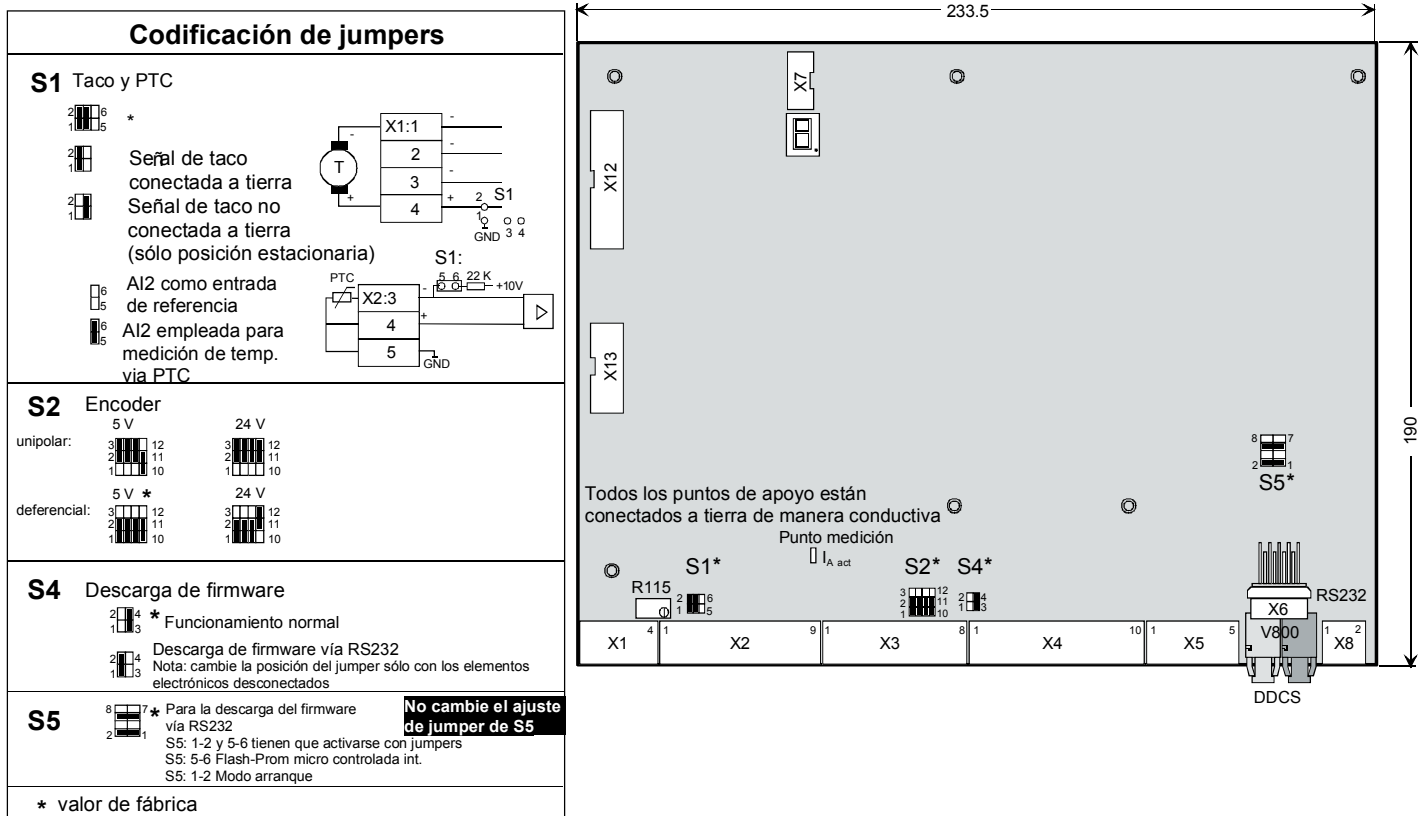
/1 Composición de la tarjeta de control SDCS-CON-3A
